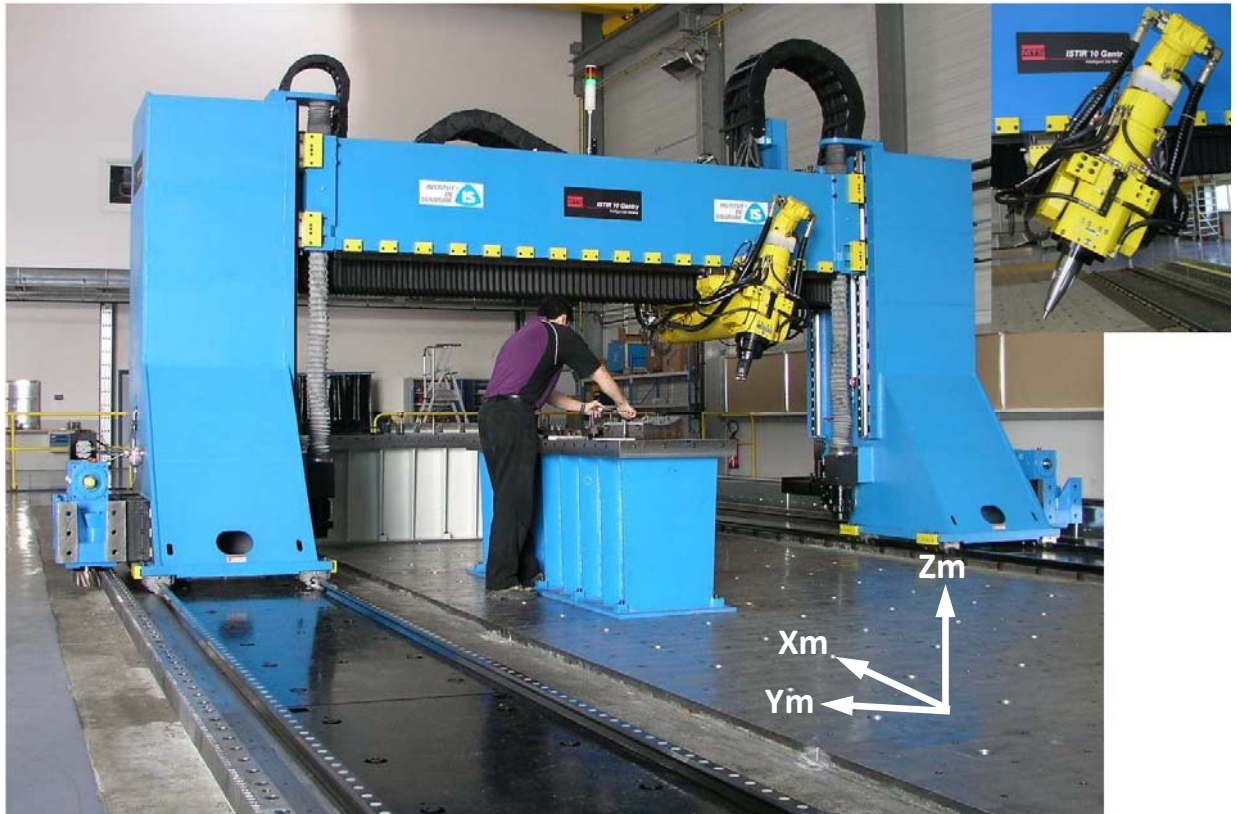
Machine MTS et tête de soudage FSW
